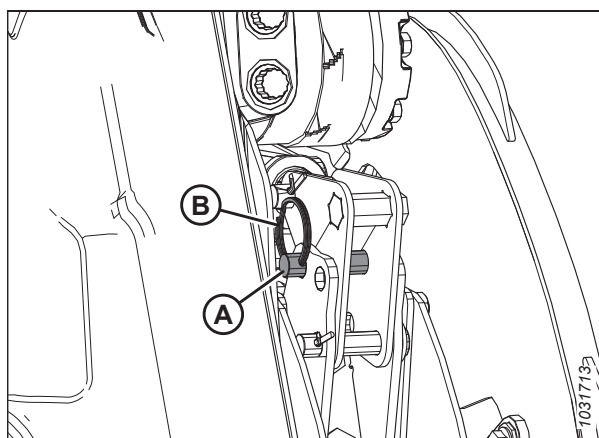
Cilindrul brațului central stâng – poziția spre spate
